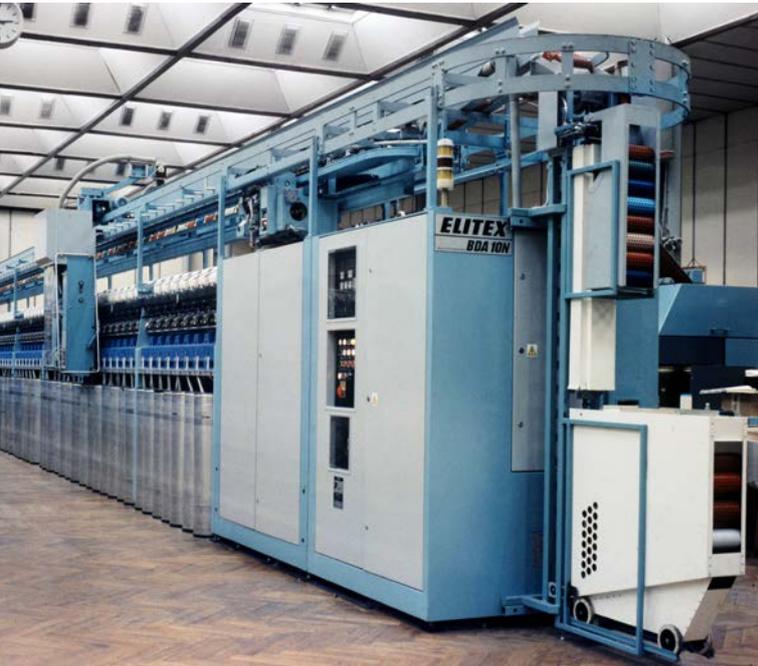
La primera máquina de hilar a rotor automática, BDA-10, con limpieza y remiendo automáticos
